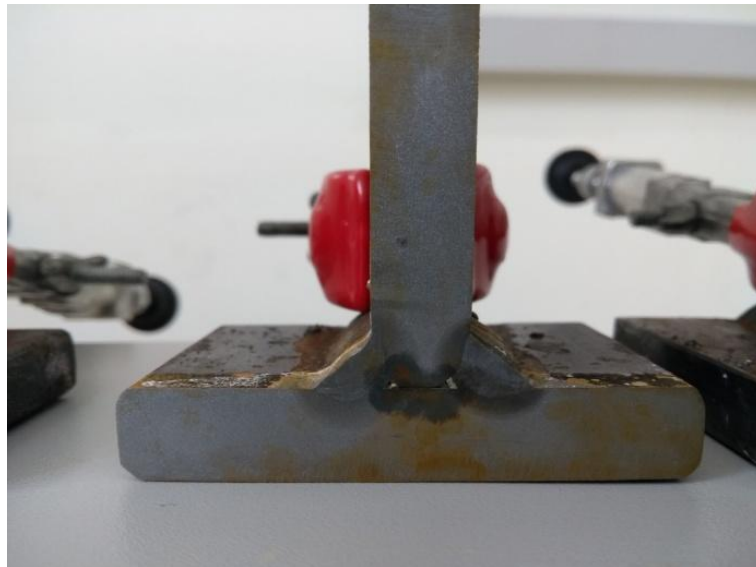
Macrografia processo de soldagem com eletrodo chapa nova.
